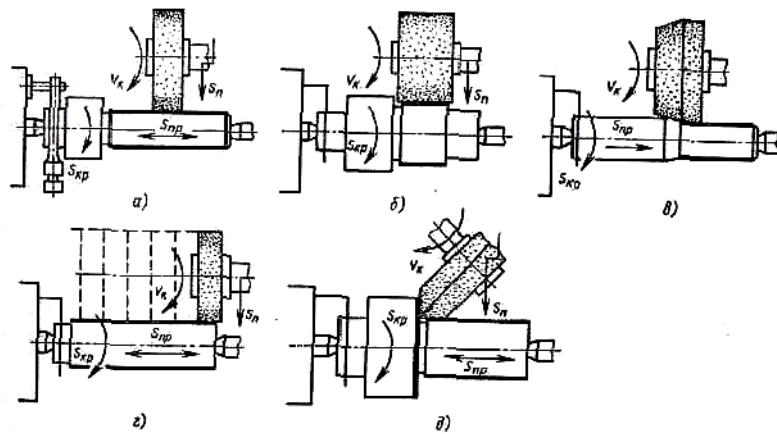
Схемы обработки наружной цилиндрической поверхности заготовок на круглошлифовальных станках
